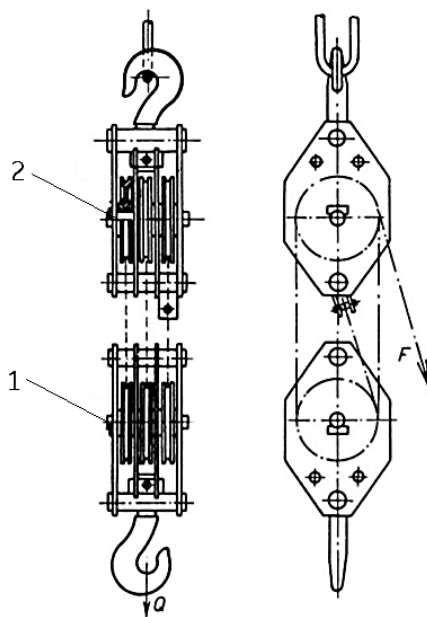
Kladkostroj s jednou kladkou volnou a jednou kladkou pevnou
